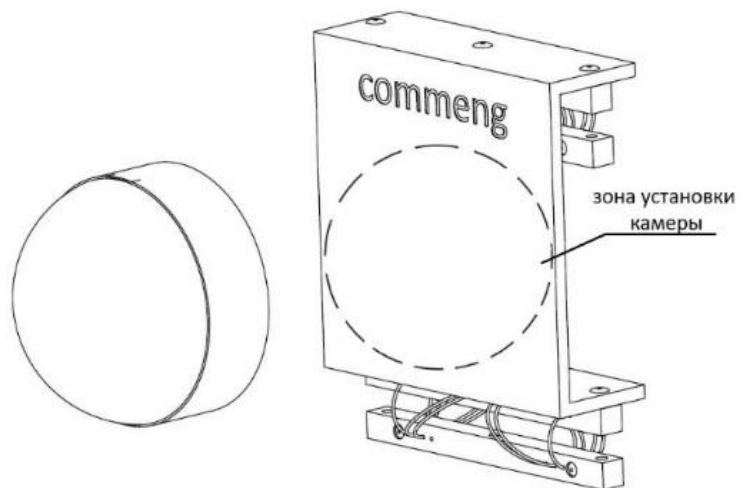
Установка оборудования (IP-камеры) на монтажную площадку
